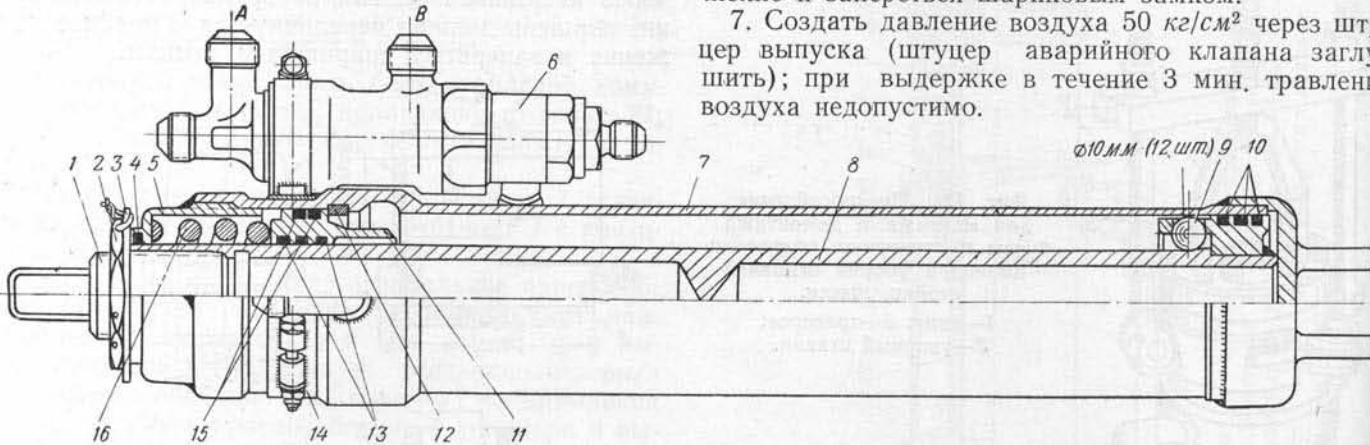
Направляющая втулка для установки штока с поршнем в цилиндр с навертной крышкой.
